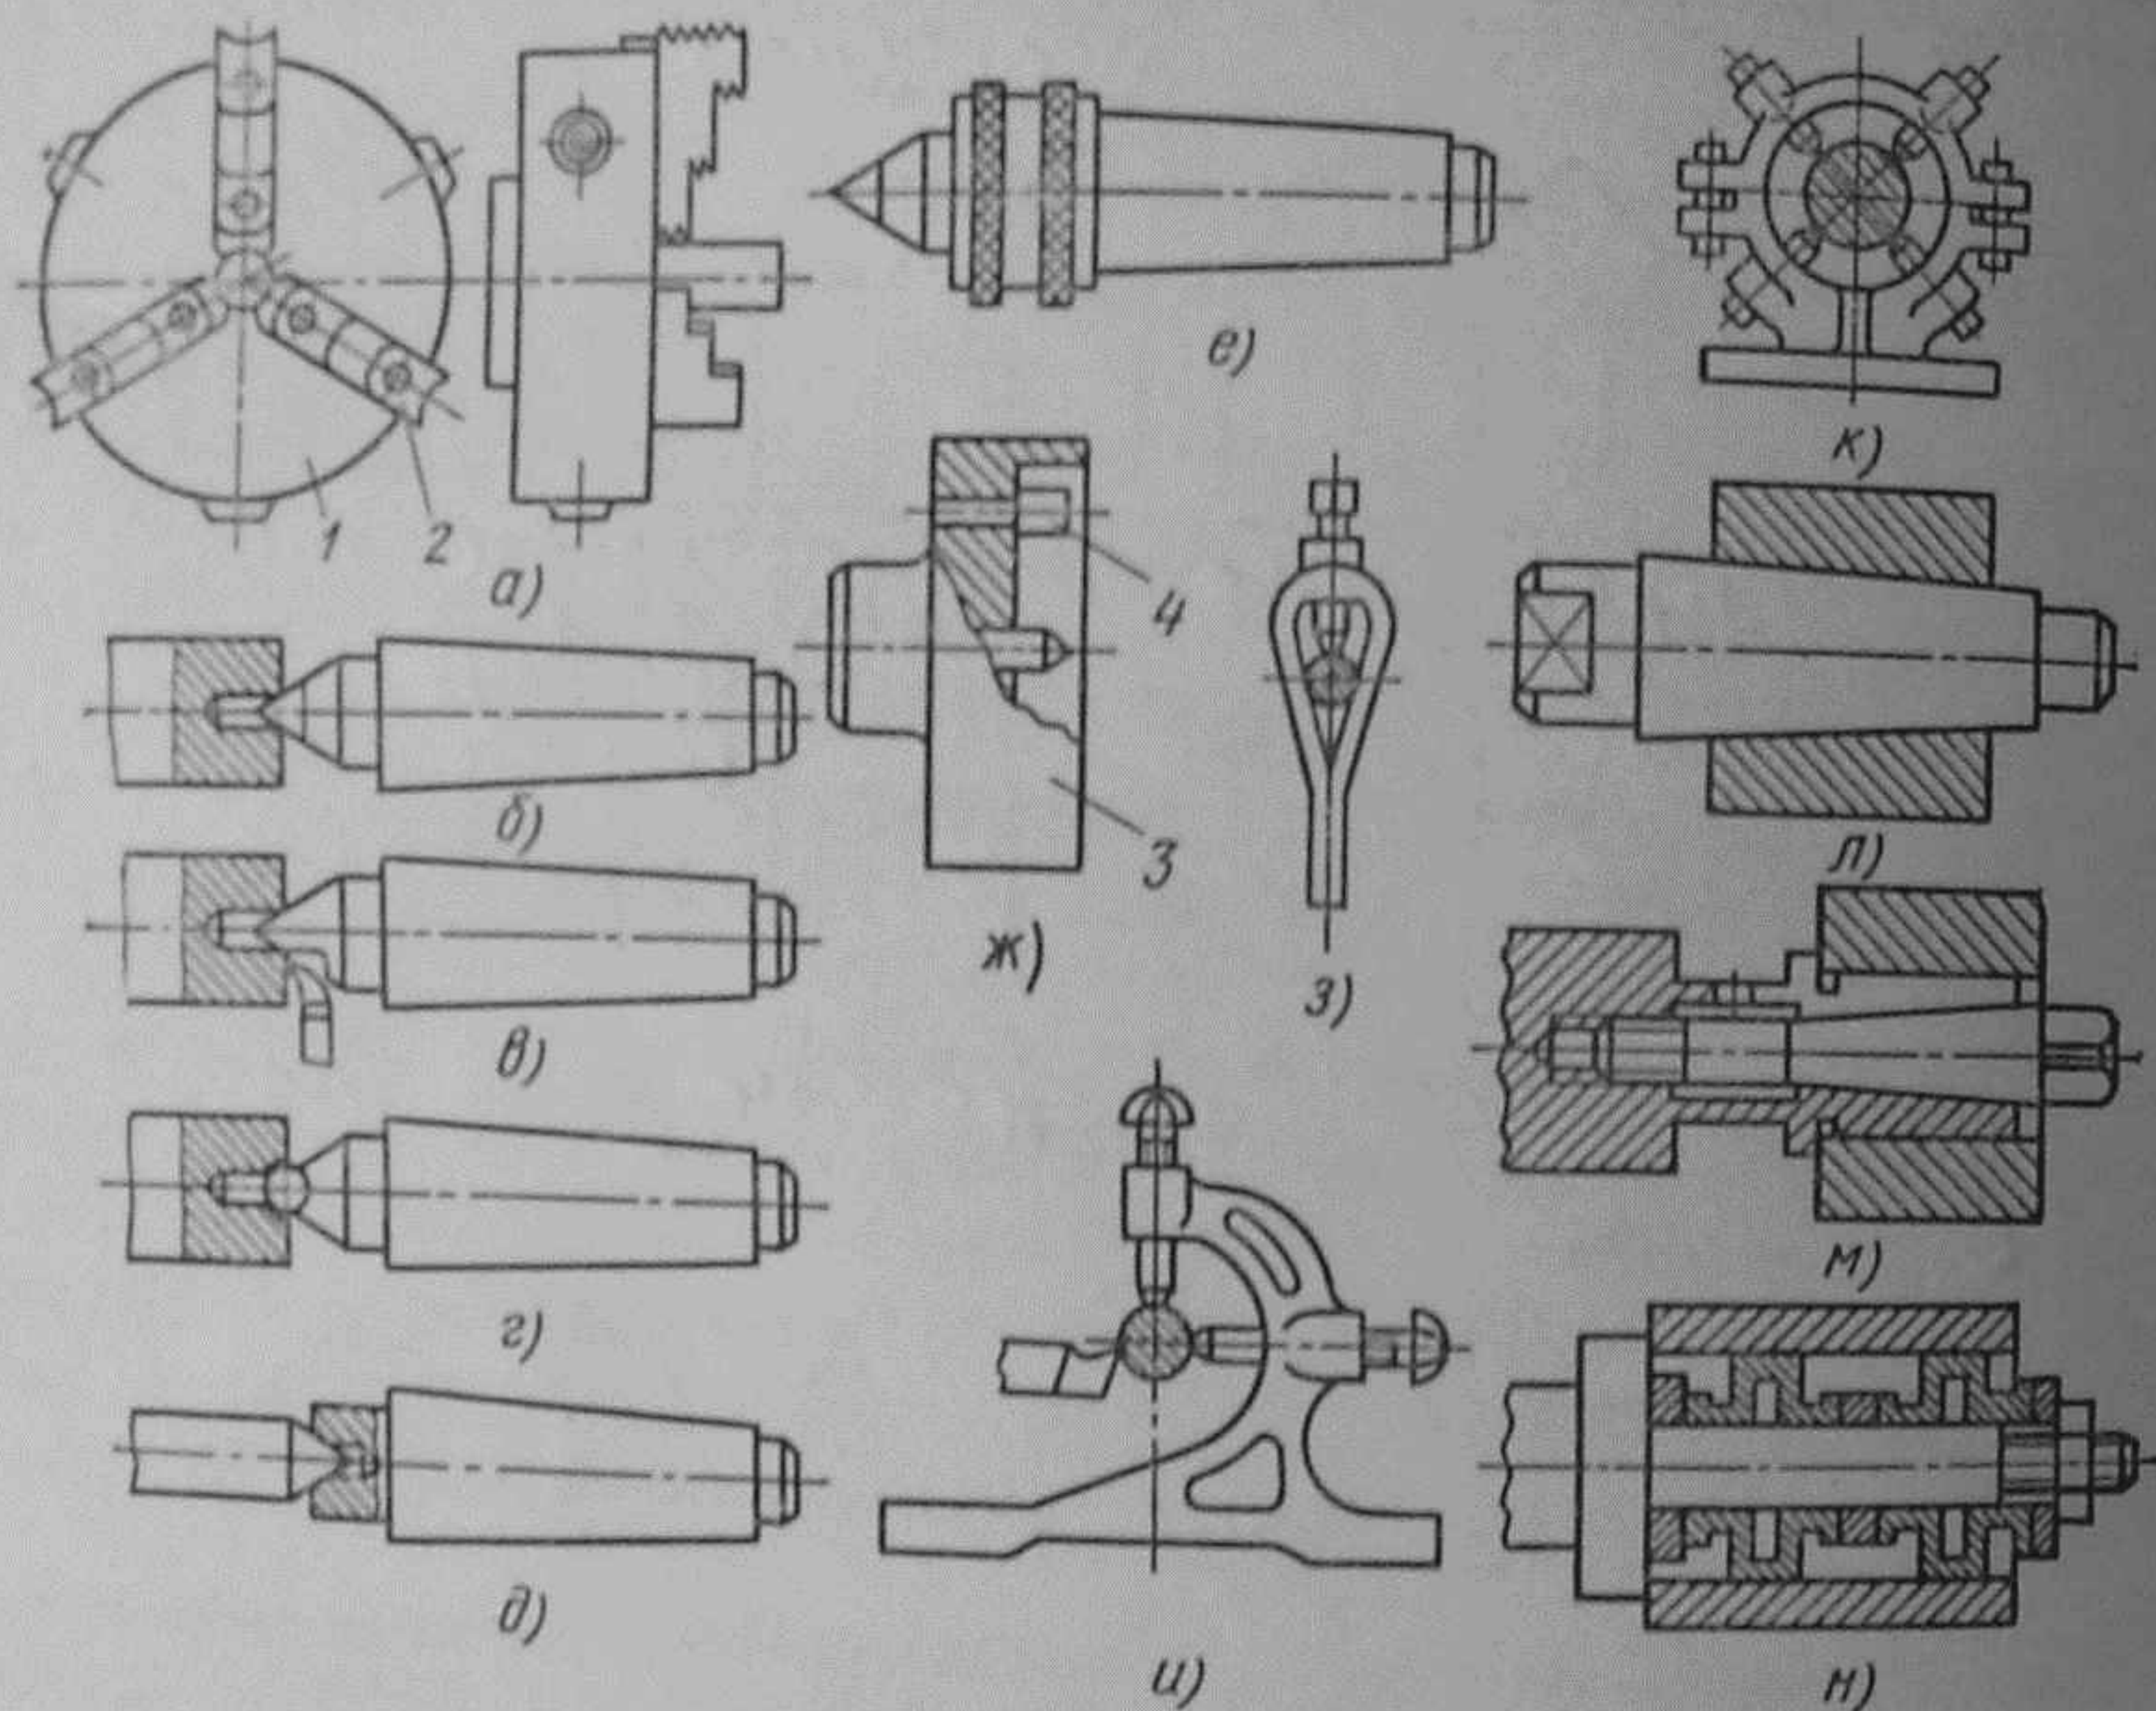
Приспособления для закрепления заготовок на токарных станках
